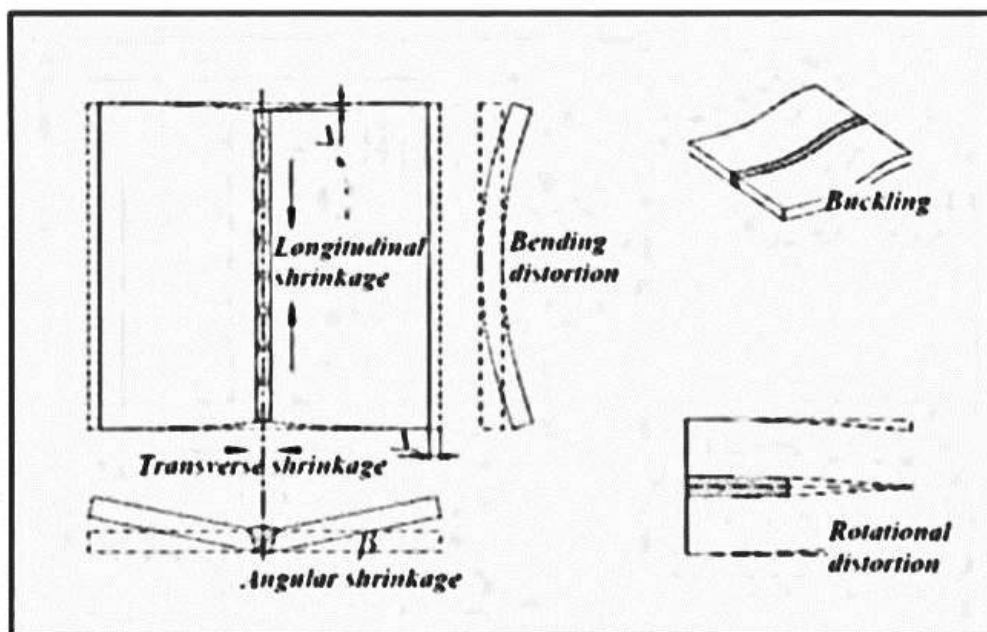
Types de retraits dus au soudage [19, 26]
